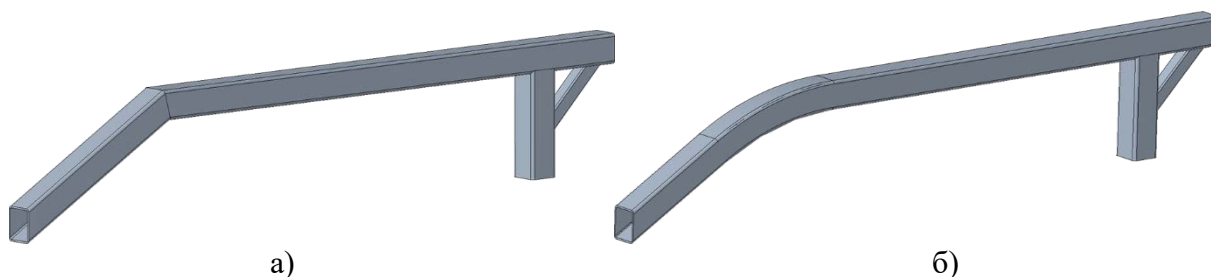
Фінальний конструктив балки кріплення, де а - зварювальний варіант, б - згинання
